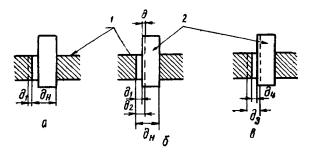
Слабина щеток в обоймах щеткодержателей: a — отклонения и допуски обоймы; b — отклонения и допуски щеток; b — слабина щетки в обойме; b — обойма; b — щетка; d — номинальный размер.
